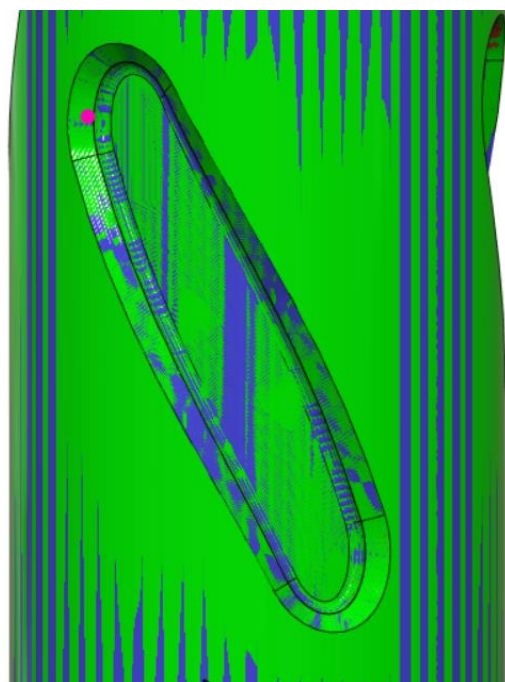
Místo vzniku neopravitelné vady u 4D operaci,
